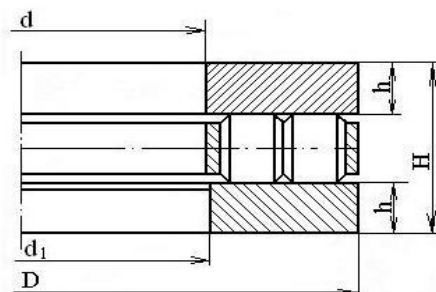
Подшипник роликовый упорный двухрядный
